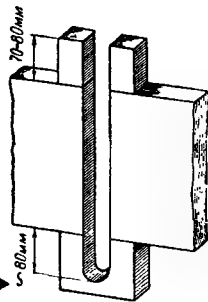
Расположение выводных планок при электрошлаковой сварке
